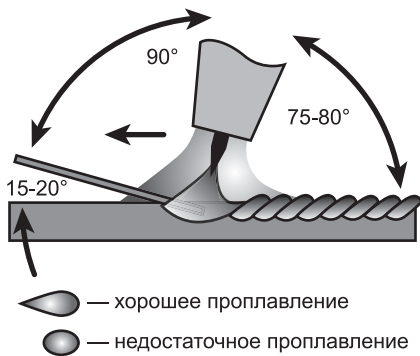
Положение горелки и присадочного прутка при TIG сварке, вид формы сварочной ванны
